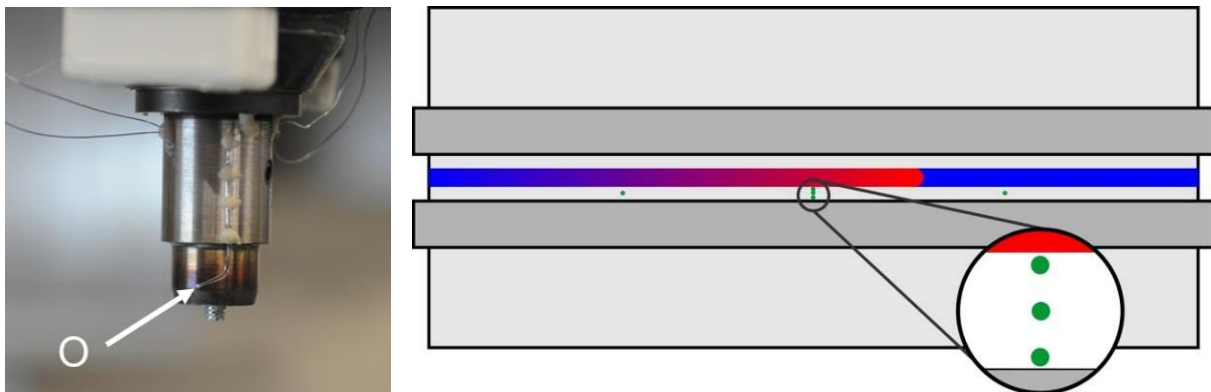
Thermoelement am Schweißwerkzeug für Al2024 (links); Positionierung der Thermoelemente (grüne Punkte) im Blech
